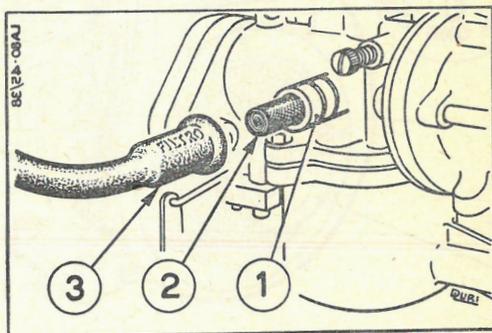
SMONTAGGIO DEL FILTRO SUL CARBURATORE
